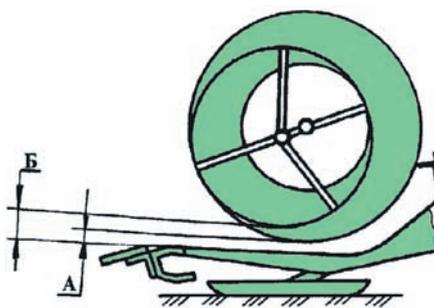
Схема расположения шнека и его пастьково-го механизма при работе жатки. А-зазор между спиралью шнека и днищем корпуса; Б-зазор между пальцами пастьково-го механизма и днищем корпуса
